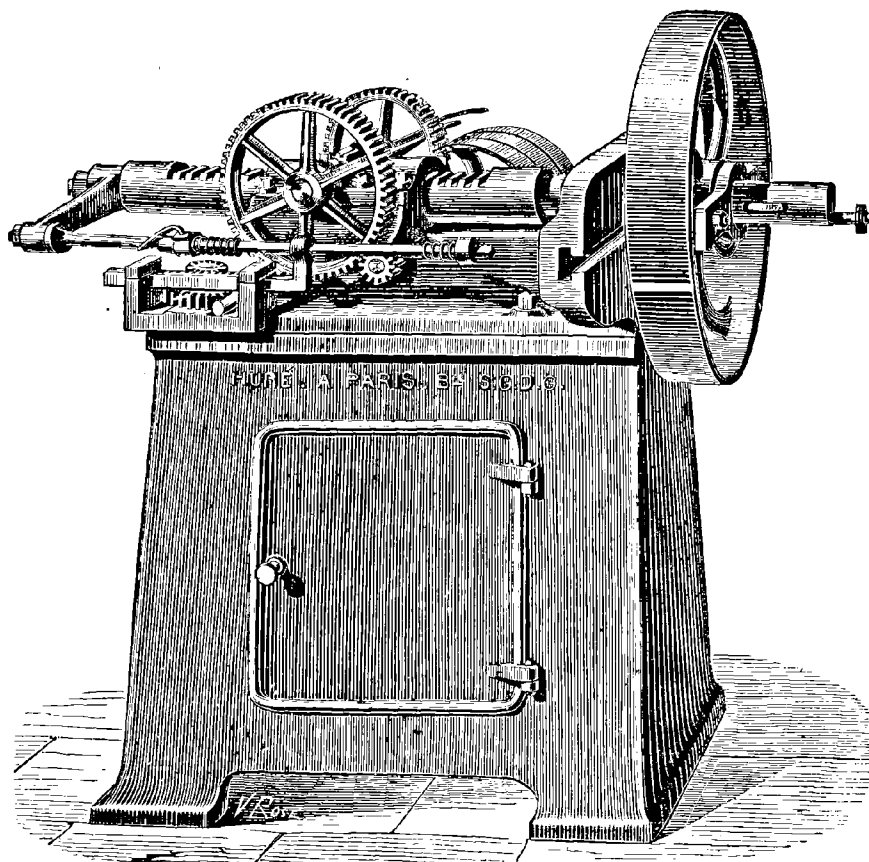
Machine à canneler à mouvement automatique de M. Huré.
